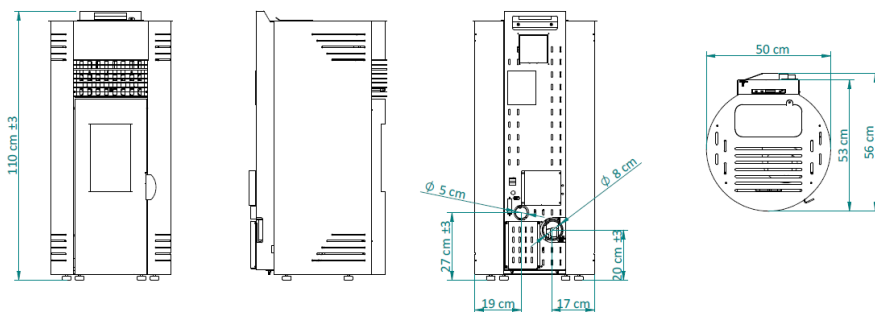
E – Dimensiones de la estufa de pellets Indie 8 kW
